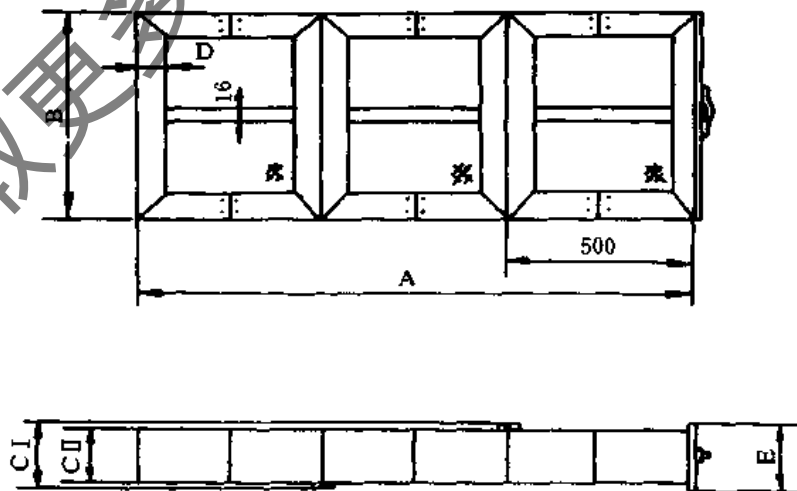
FK-57 型空气处理机过滤器外形尺寸
